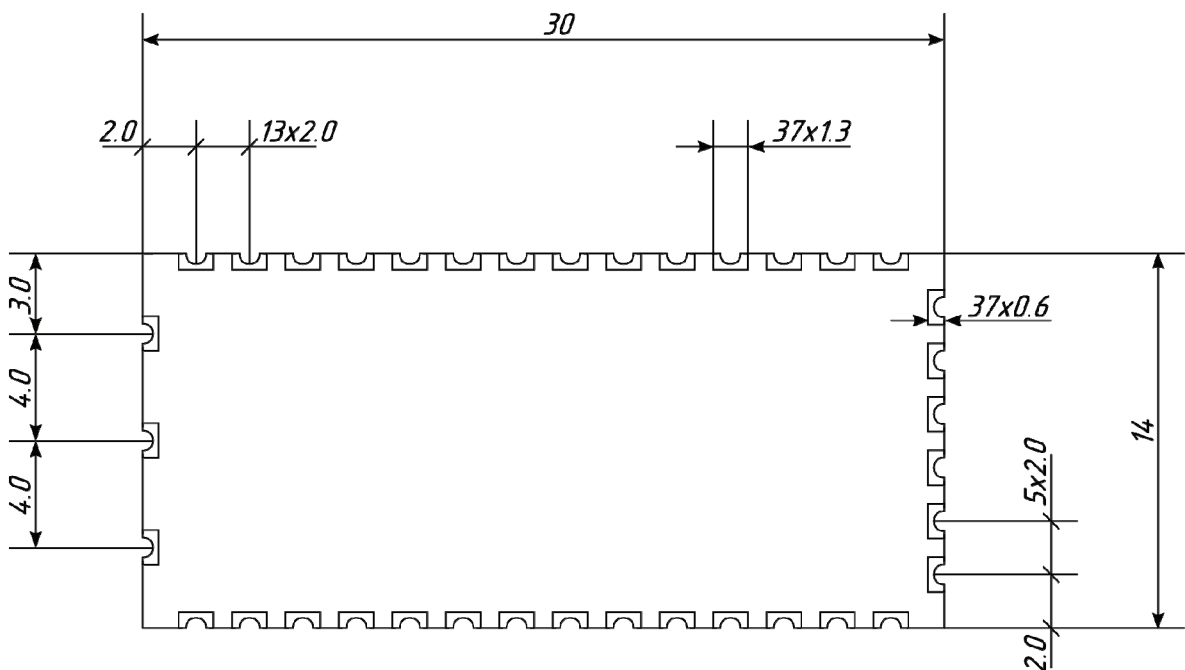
Присоединительные размеры модуля TE-CC430F51-433
